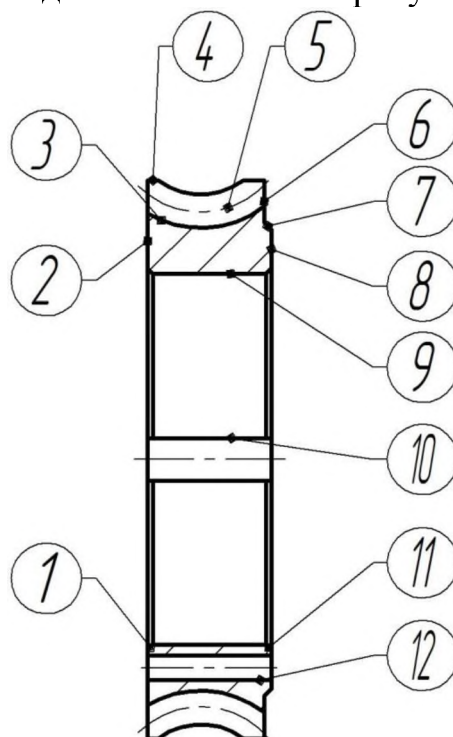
Позначення поверхонь деталі колесо черв'ячне
